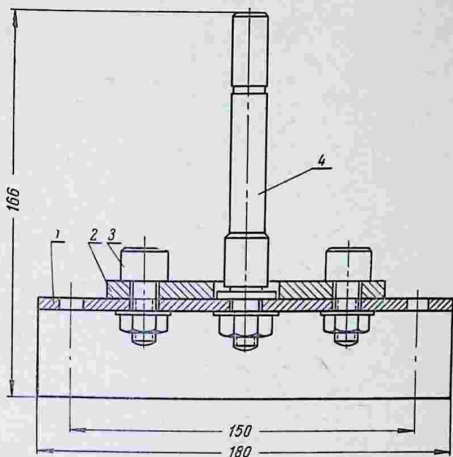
Приспособление для разборки и сборки ротора масляной центрифуги:
